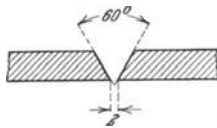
V-förmige Vorbereitung der Schweißfuge.
